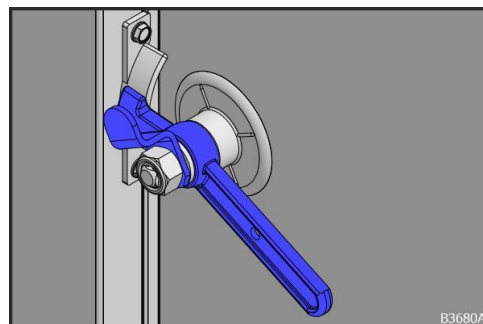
Nockenzunge mit Innenhebel und Fanghaken (druckseitig)
